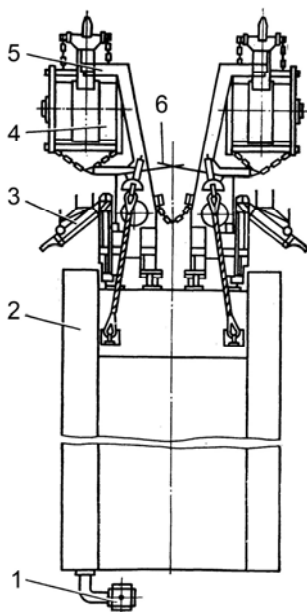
Катково-ножевой минный трал КМТ-7:
